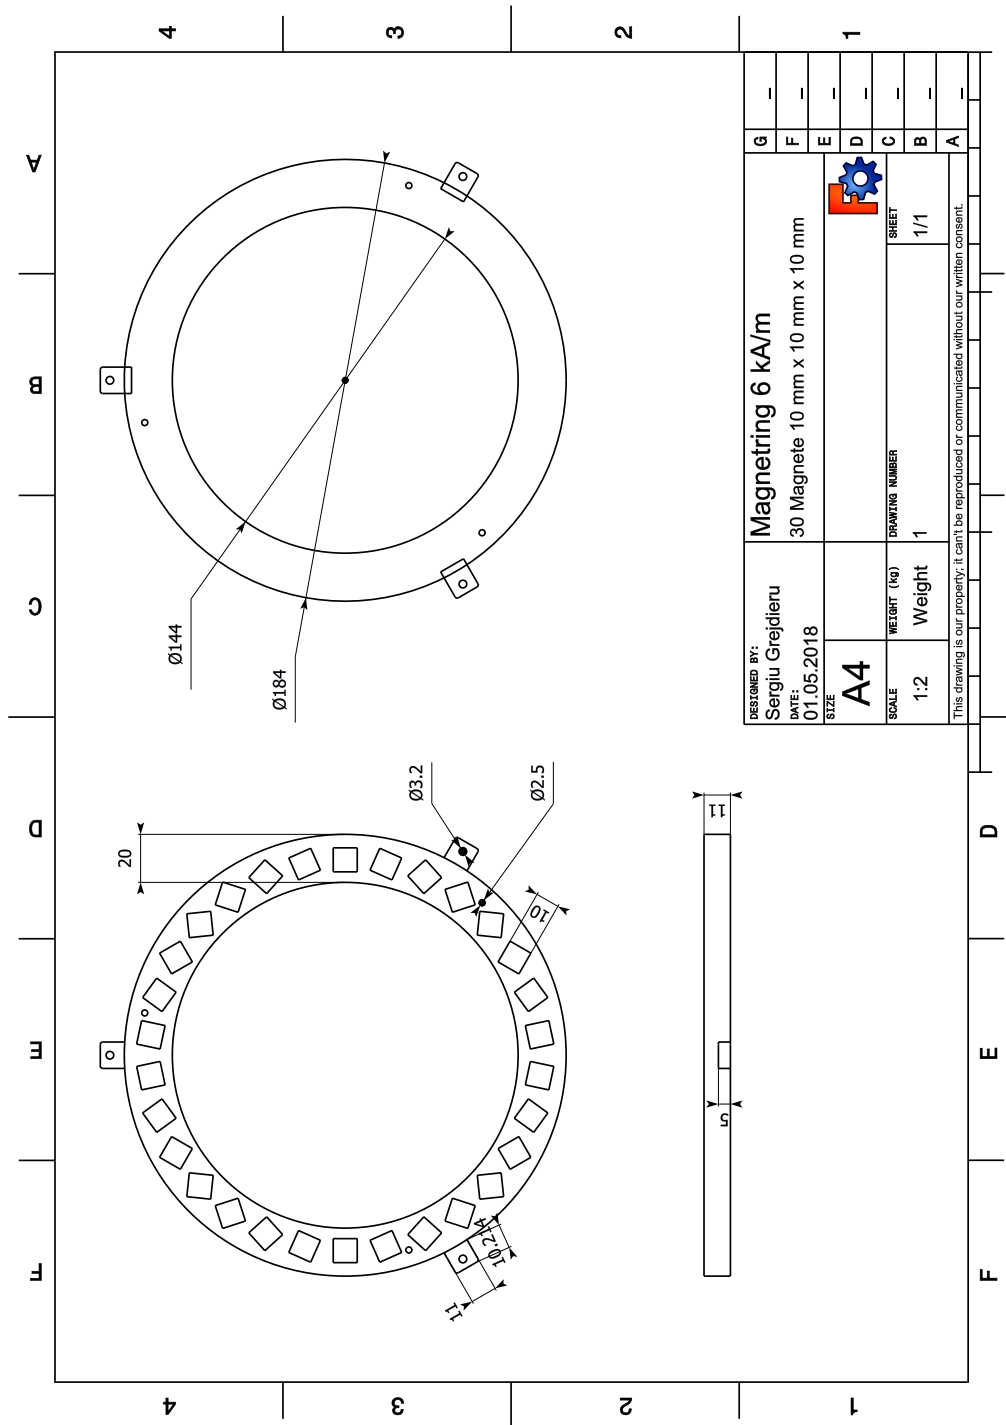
Technische Zeichnung: Magnetring 6 kA/m
